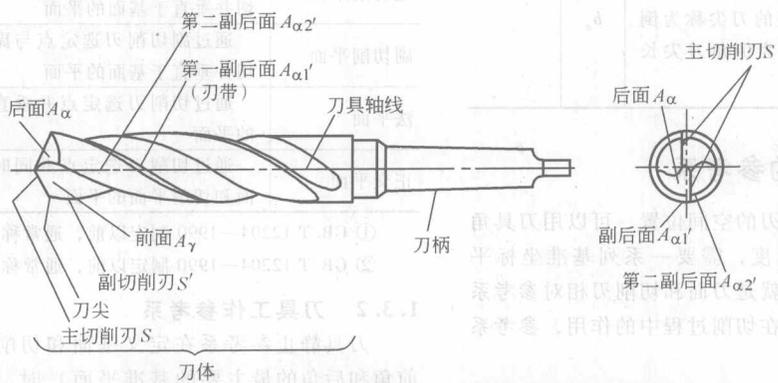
麻花钻切削部分上的切削刃和刀具表面
